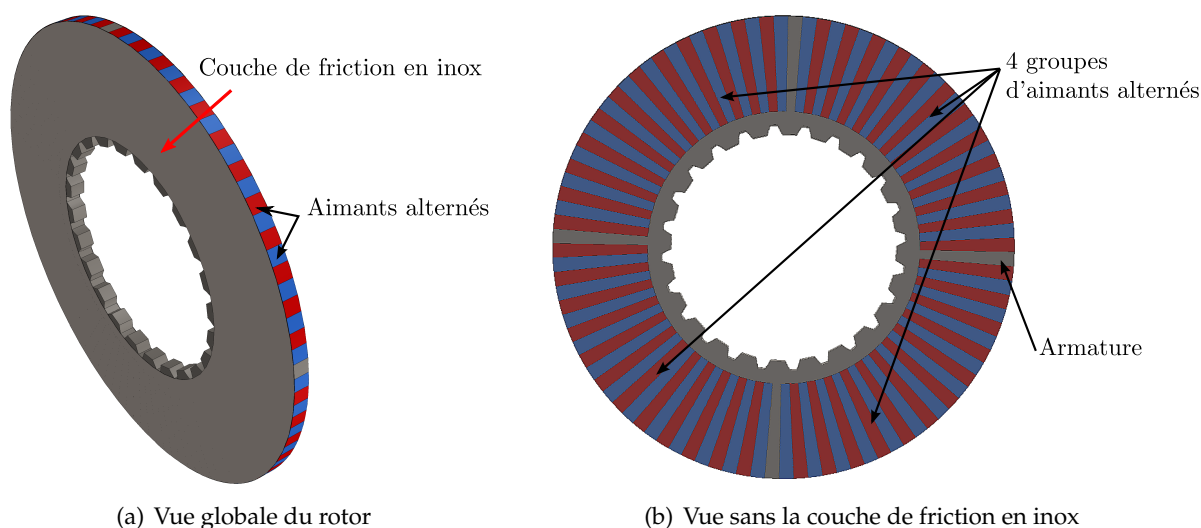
Vues 3D du rotor du prototype laboratoire
